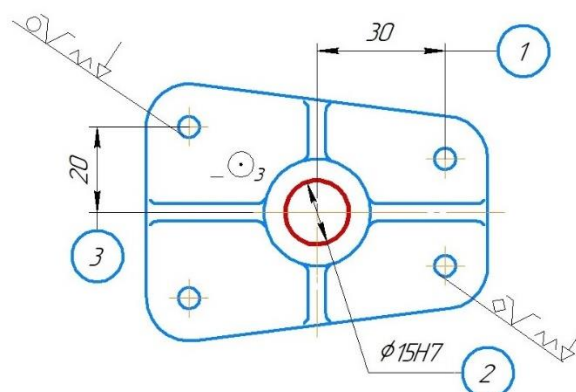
Схема базування та закріплення заготовки для операцій механічної обробки деталі «Кришка»
